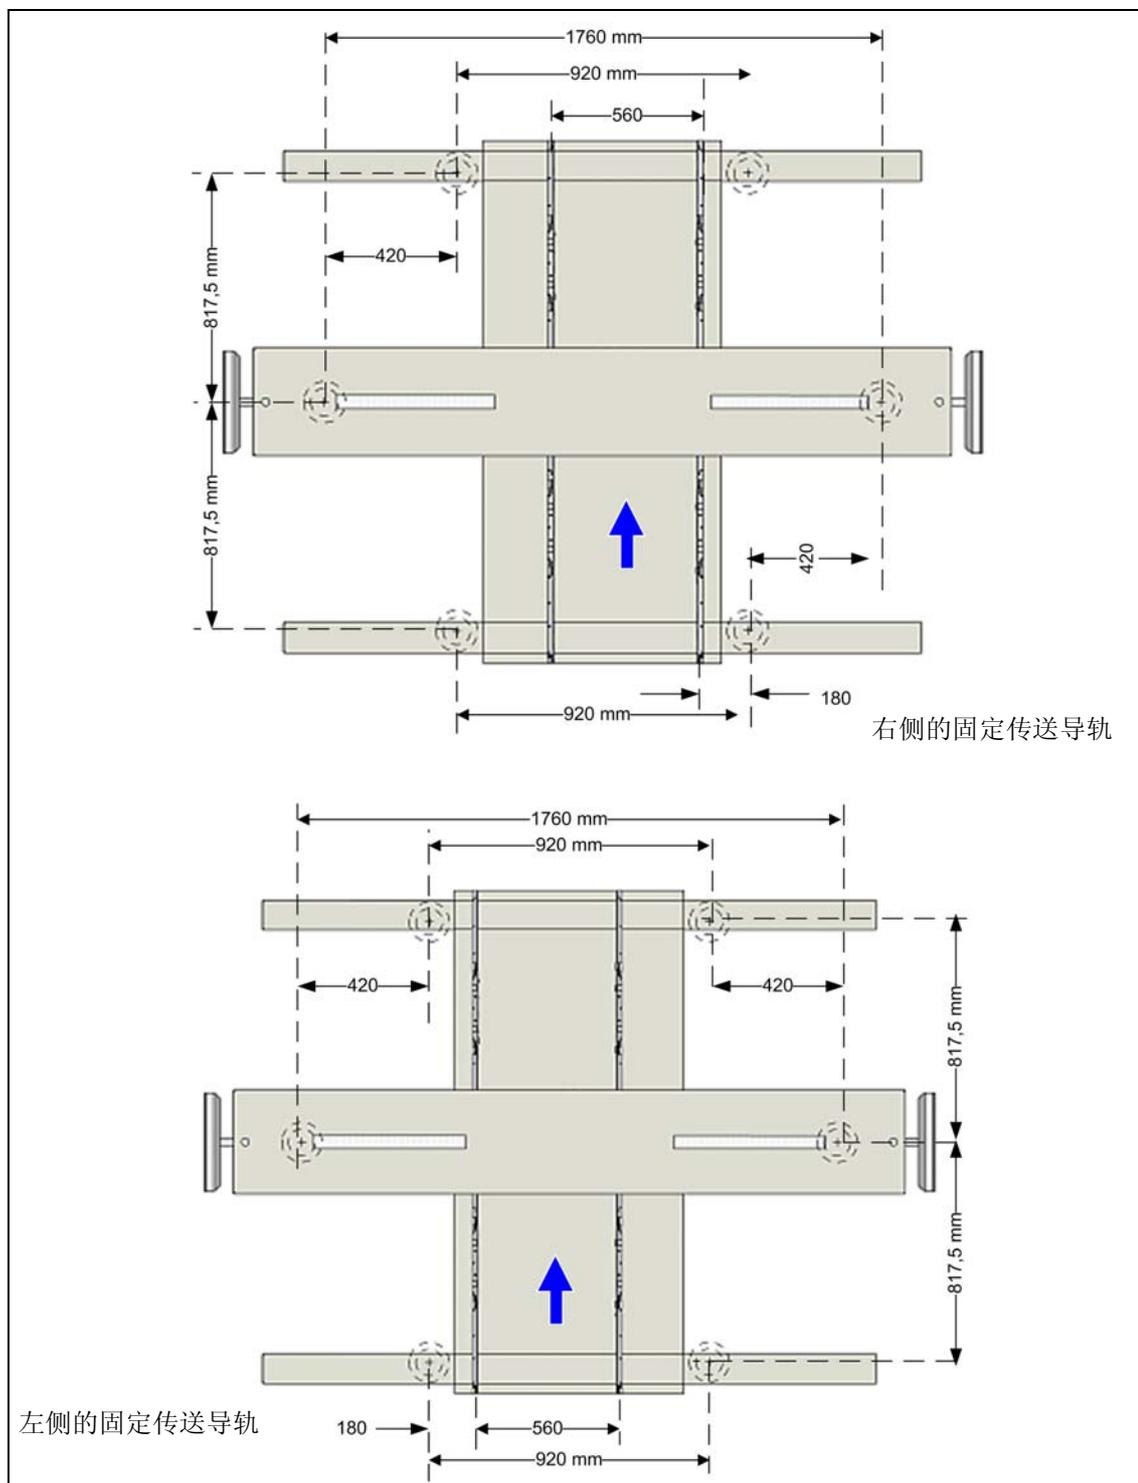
8 PCB 单传送导轨的贴片机支脚间隙 (单位毫米)
